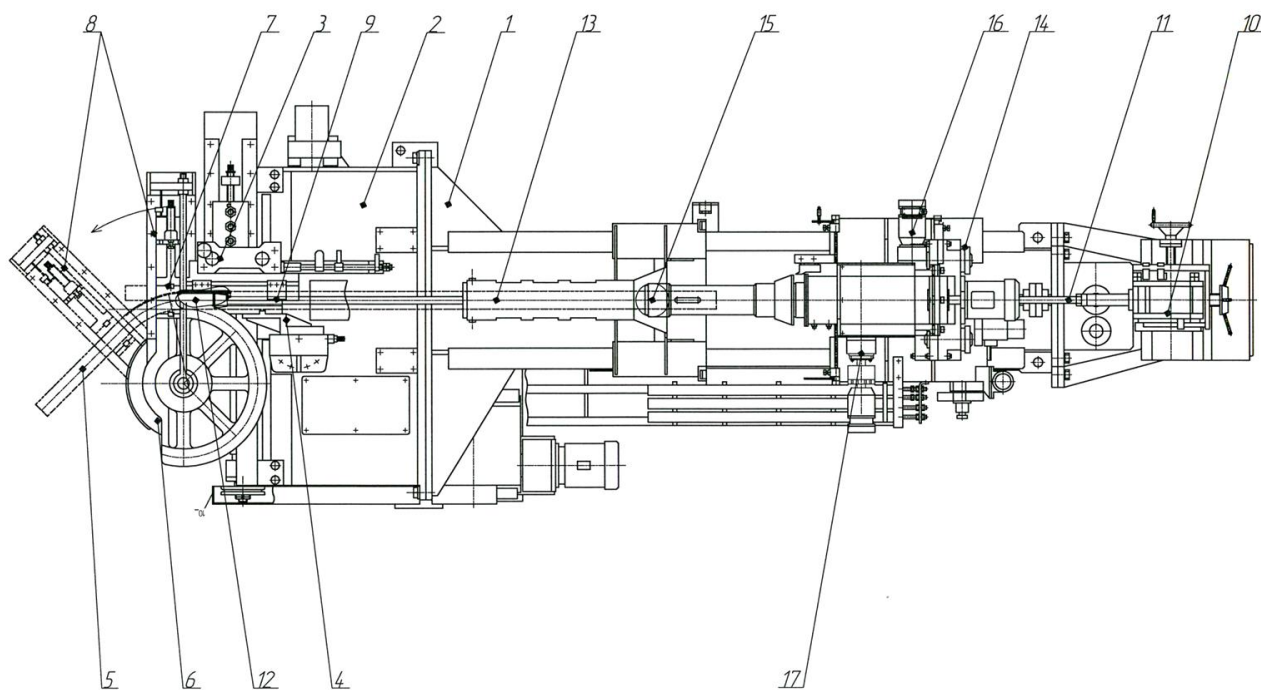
Предложение по модернизации трубогибочного станка СТОПН-80, вид сверху
